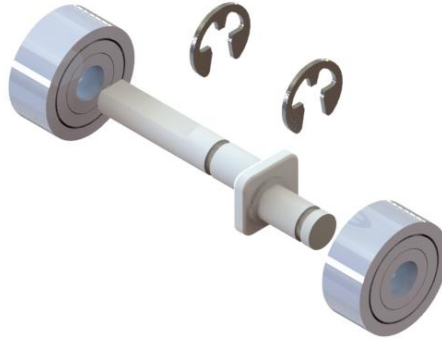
Explosión del ensamble del seguidor excéntrico.
